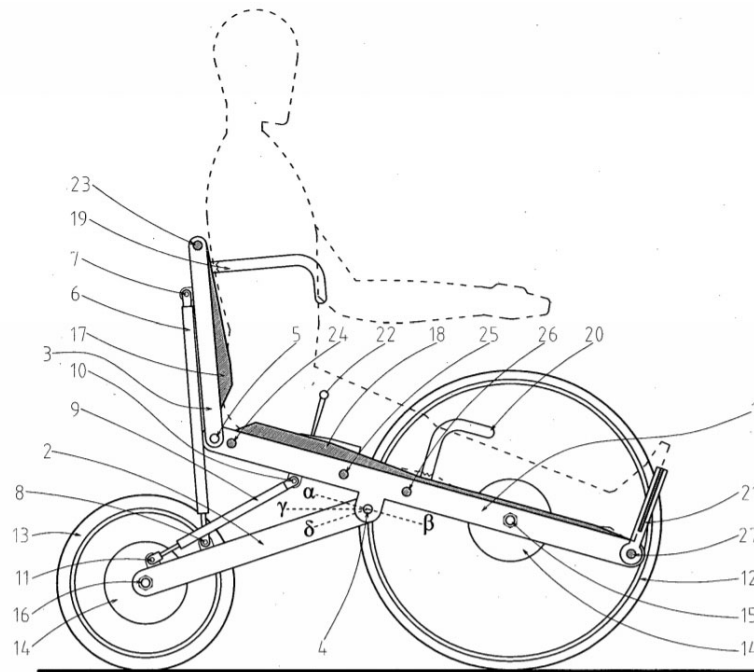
Posición horizontal de la silla de ruedas. [Petrotos, 2016]
